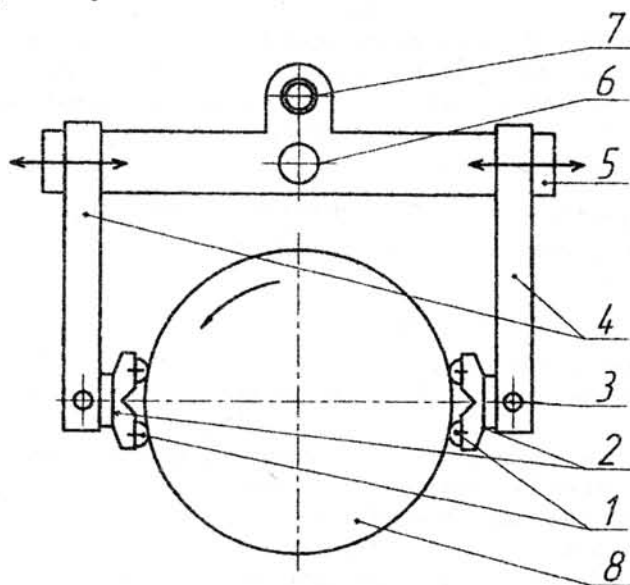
Устройство для обработки покрытия вала: 1 - деформирующие элементы, 2 - державки, 3 - оси, 4 - консоли, 5 - поперечная балка, 6 - направляющая, 7 - ходовой винт, 8 - обрабатываемый вал.
